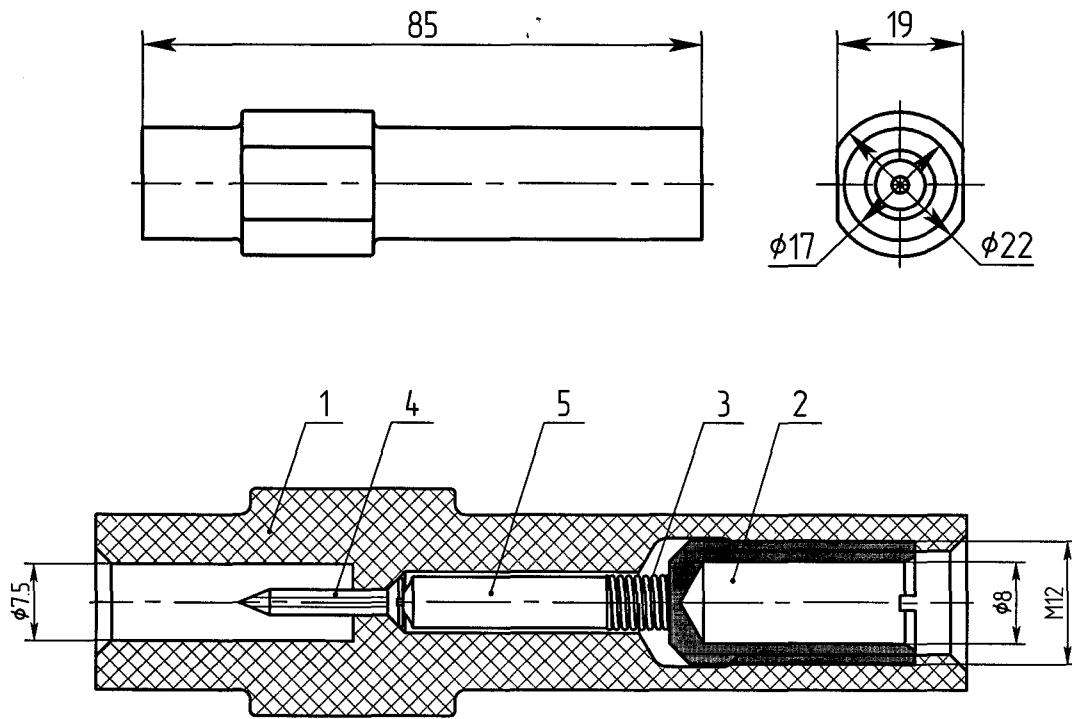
Внешний вид и установочные размеры прибора щитового исполнения
